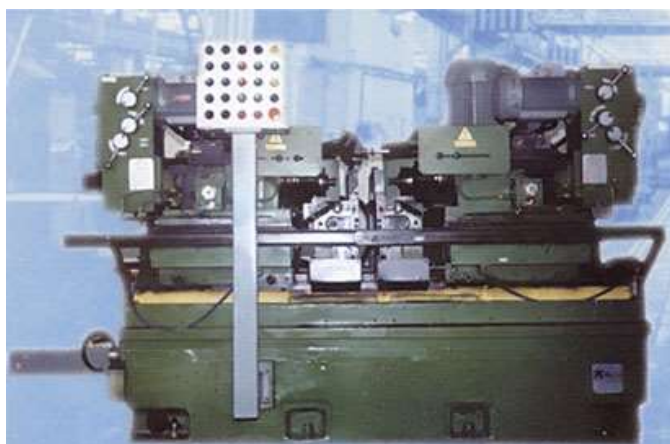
Фрезерно-центровальный станки 2Г942
